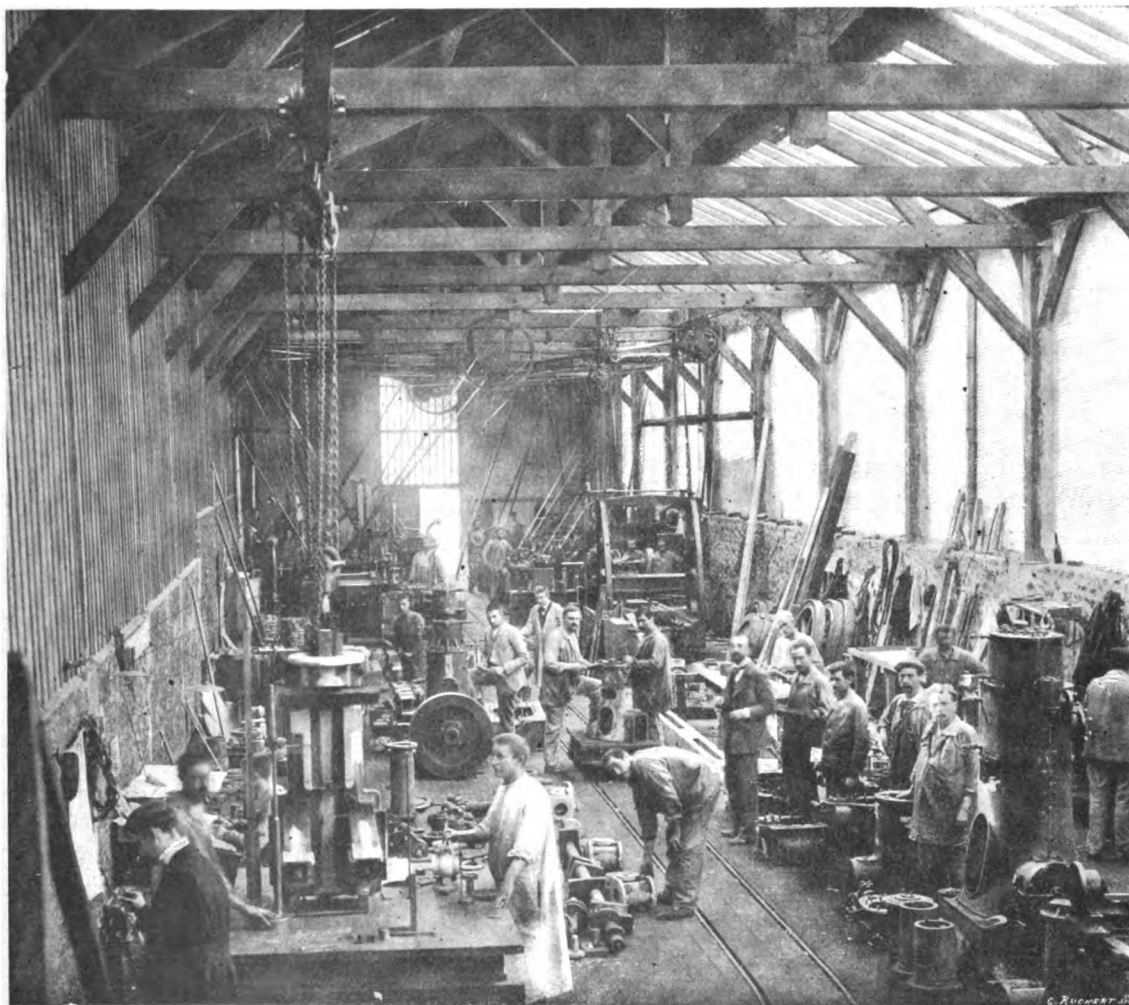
Vue des ateliers Boulte et Larbodière, à Aubervilliers.
